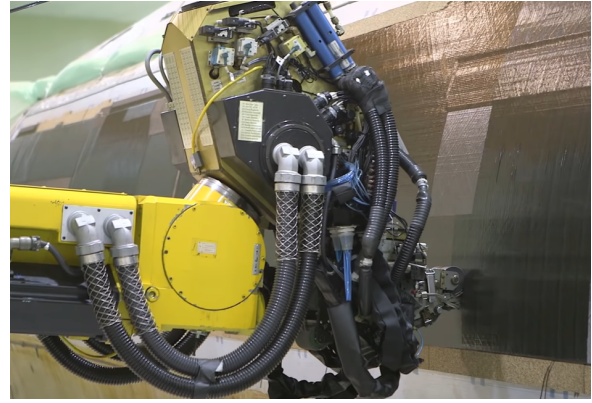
Techniques de fabrication des matériaux composites, issu de [12]
